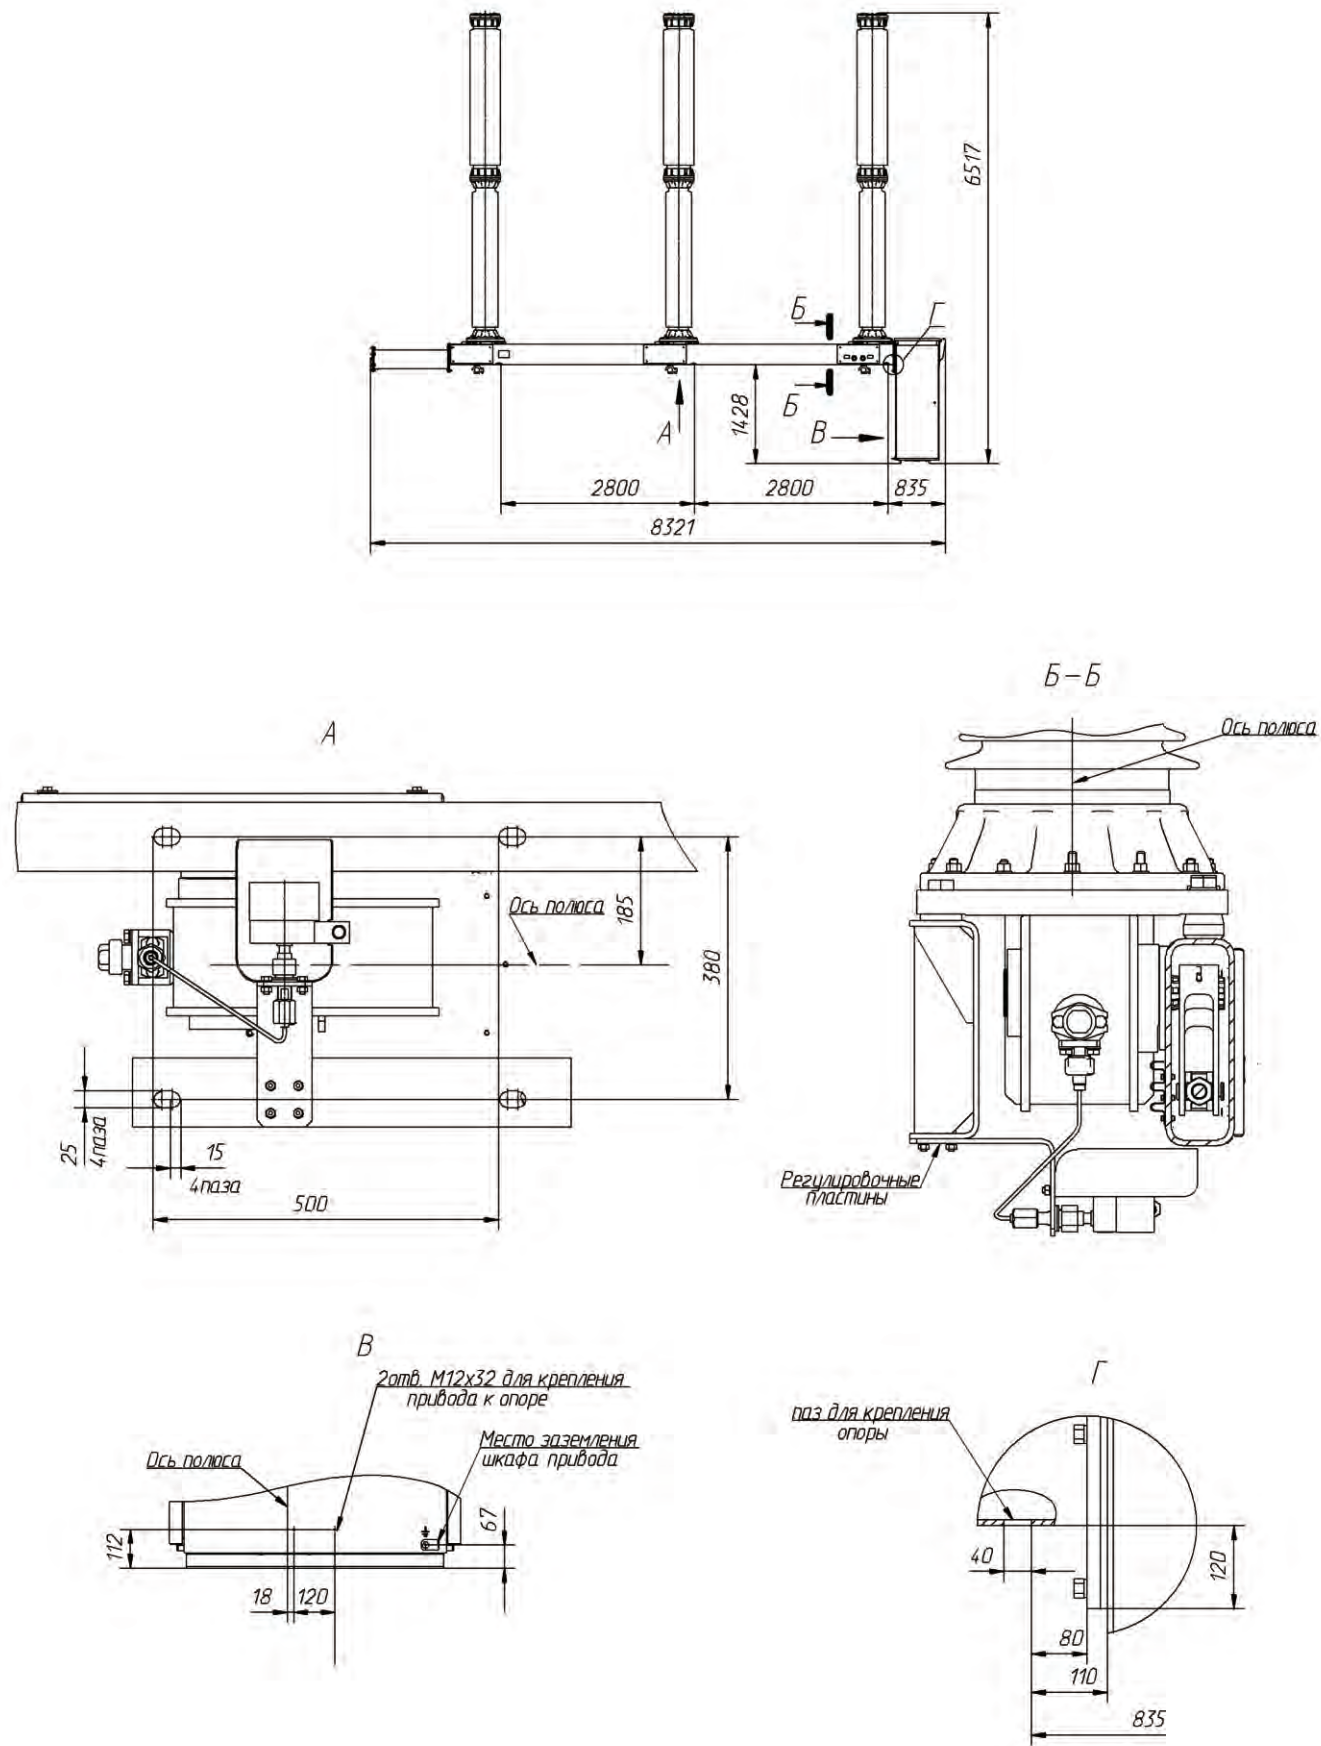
Габаритные и установочные размеры выключателя ВГТ-УЭТМ® -1А1-220 в исполнении без опорных металлоконструкций. (Неуказанные размеры см. на рис.1)
